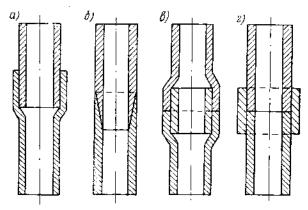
Варианты конструктивных форм сопряжений трубчатых элементов под пайку:
